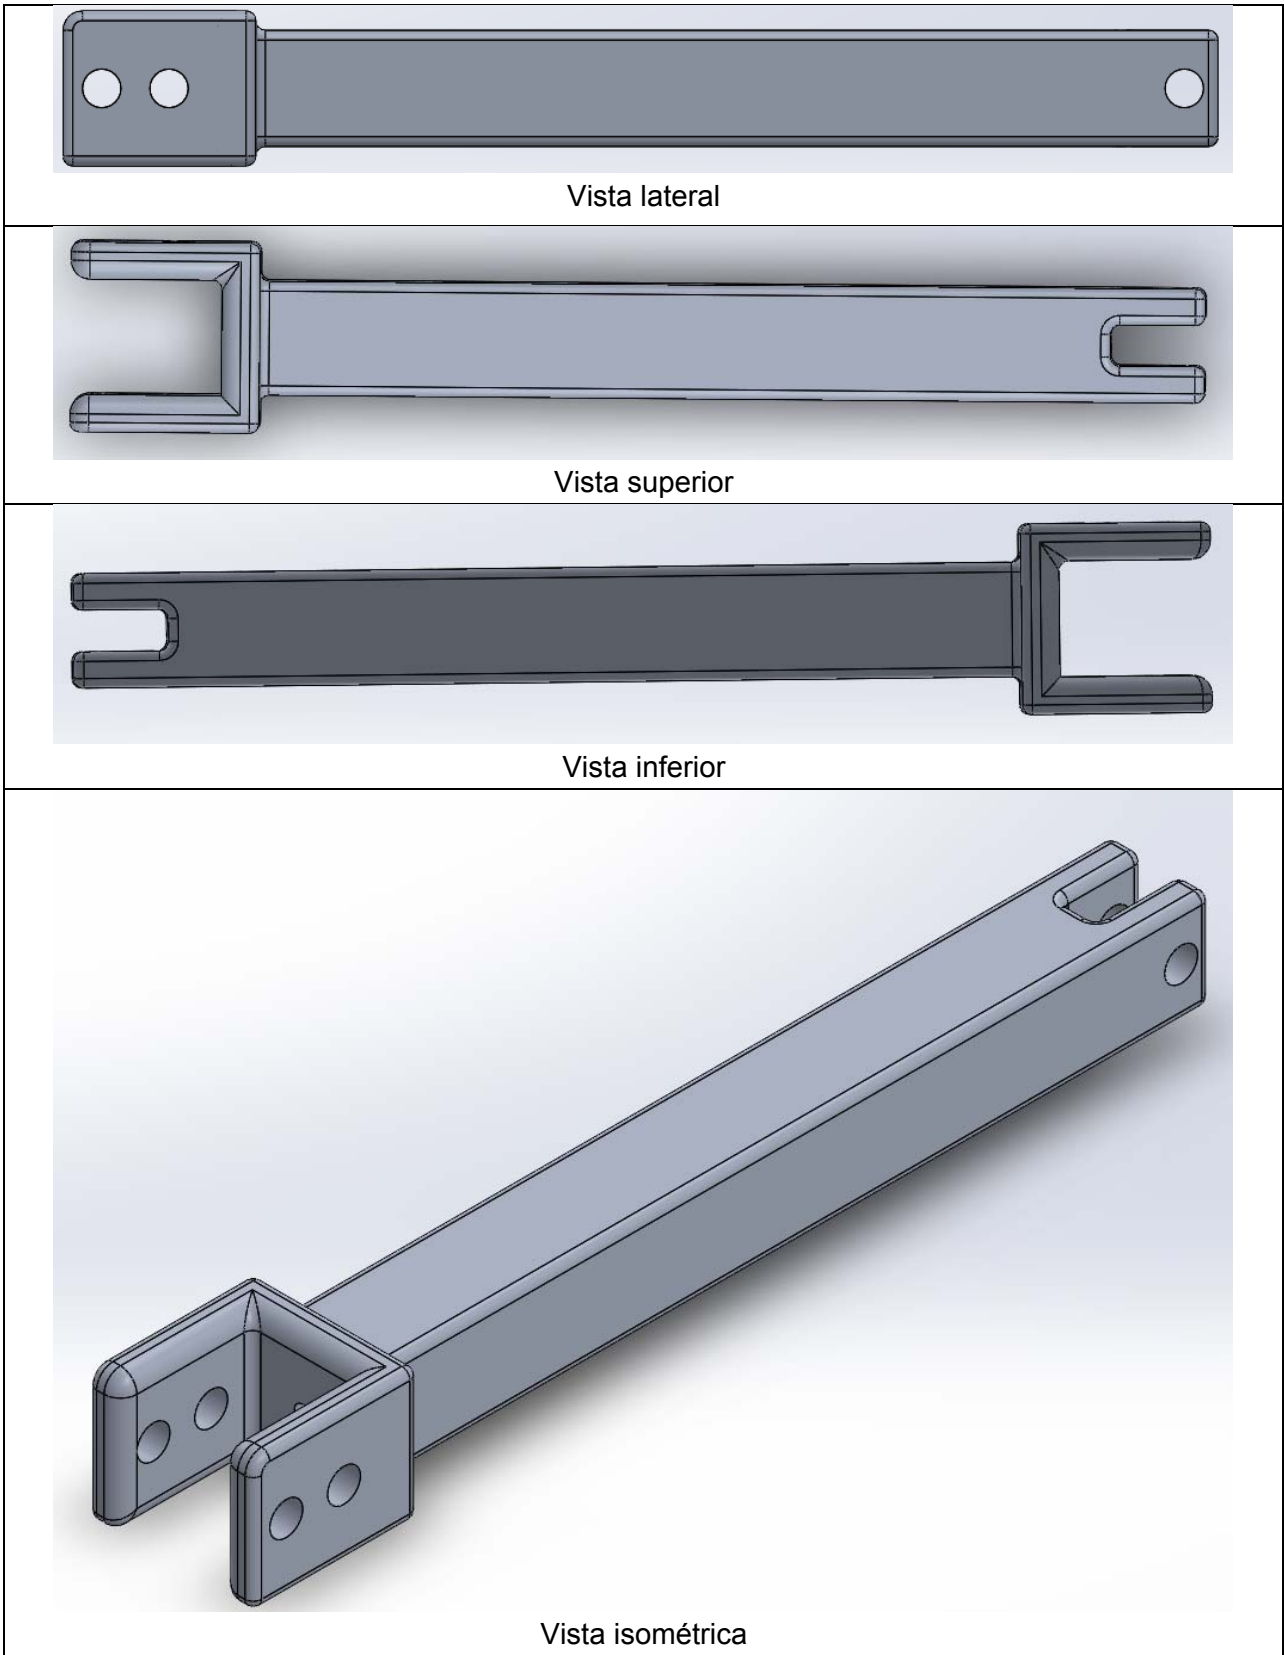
Vistas del diseño realizado en Solidworks de la extensión horizontal de brazo mecánico.
